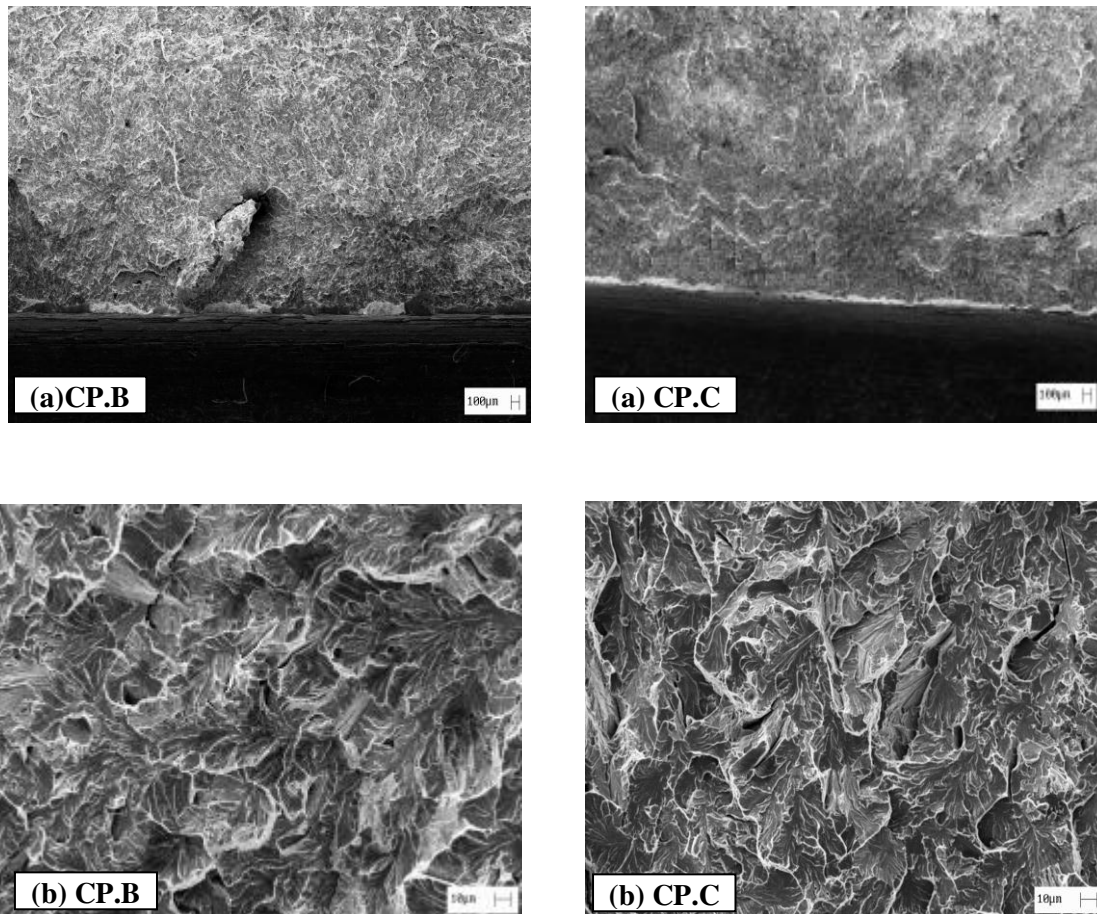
Fractografias dos corpos-de-prova B e C da roda RFo3. (a) Superfície de fratura, (b) Zona de fratura final-clivagem.
